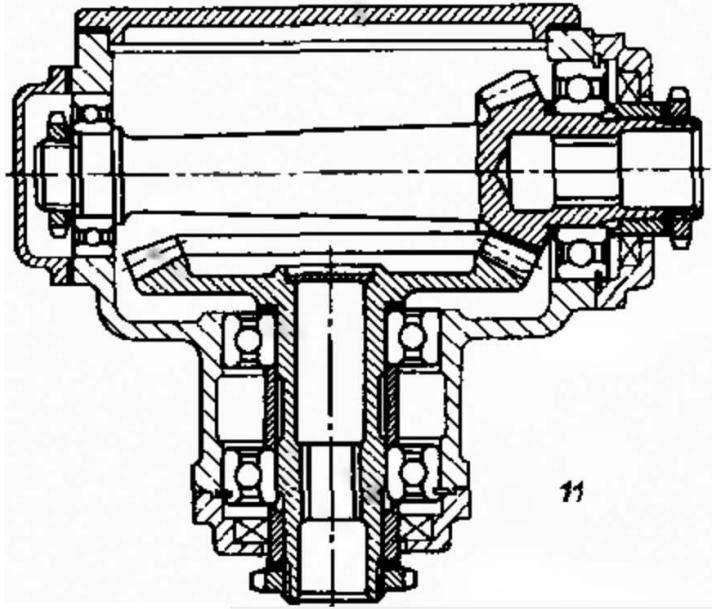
Редуктор з конічним зчепленням варіант 9
